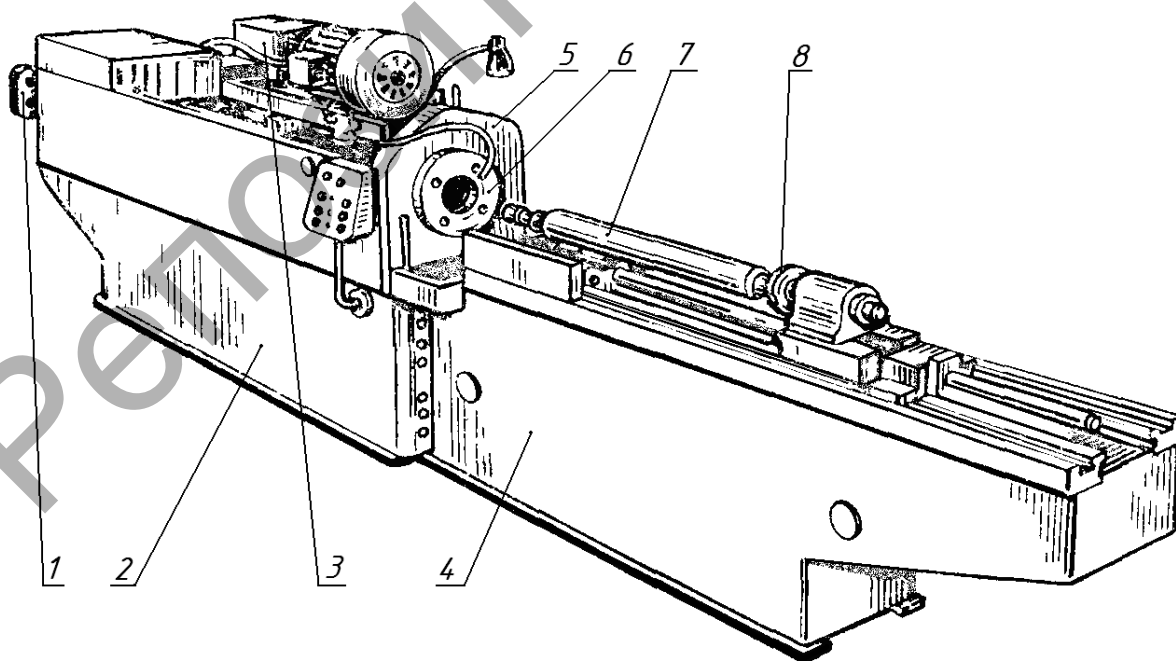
Горизонтальный протяжный станок модели 7Б57
